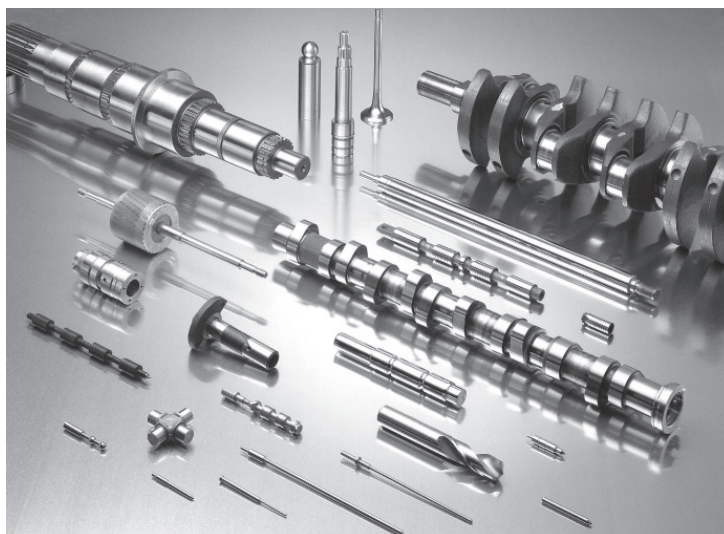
Werkstückbeispiele für die Spitzenlosbearbeitung (Quelle: Schaudt Mikrosa GmbH)
